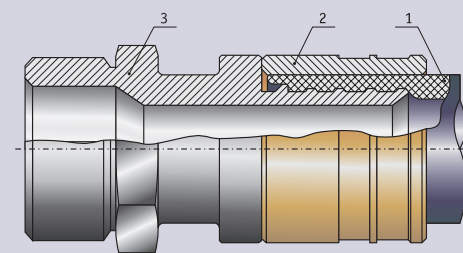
Схема соединения с натяжной латунной муфтой: 1 — труба из сшитого полиэтилена; 2 — подвижная латунная муфта; 3 — штуцер с гайкой и резьбовым хвостовиком
